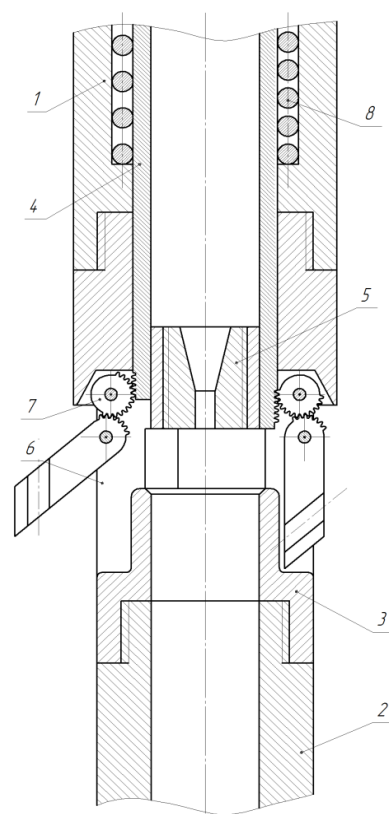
ЗУ со складывающимися лепестками шестеренчатого типа:
